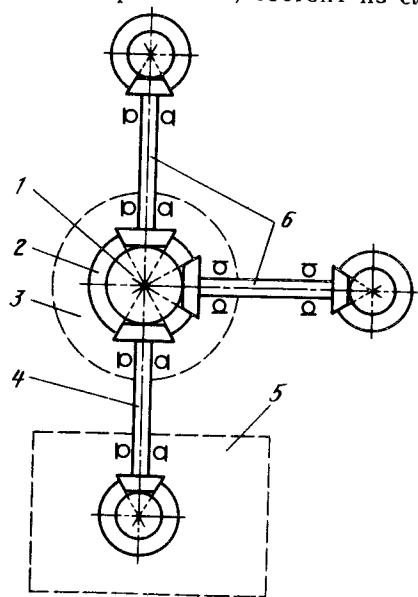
Схема размещения нескольких приводов агрегатов:
